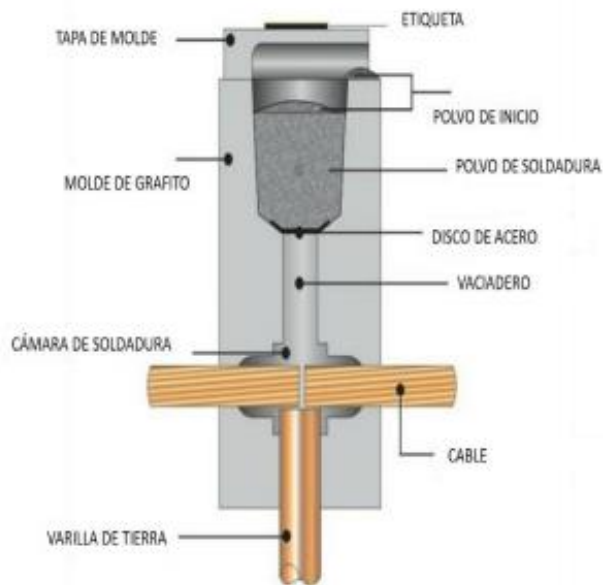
Molde de grafito para soldadura exotérmica
